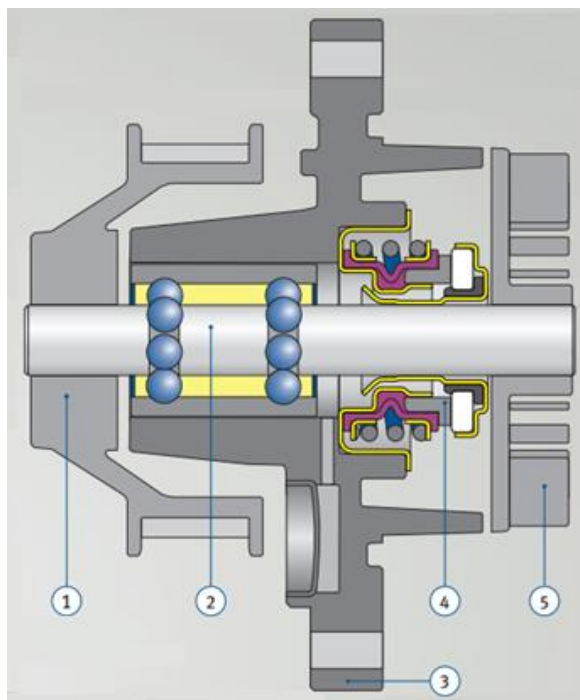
Узел крыльчатки насоса с расположением в блоке двигателя: 1- шестерня для привода зубчатым ремнем; 2 – вал с подшипниками; 3 – фланец; 4 – сальник; 5 – крыльчатка насоса
